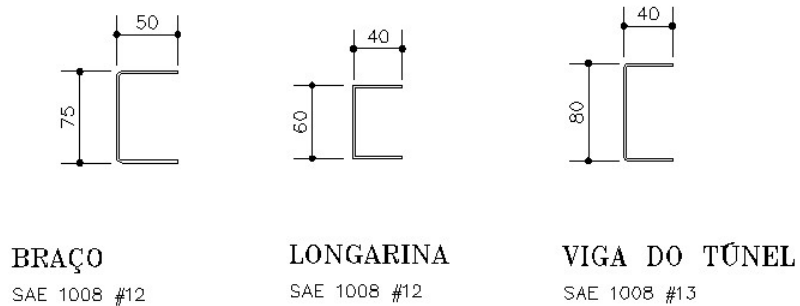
Seções transversais das vigas utilizadas no sistema (Águia (2004)).
